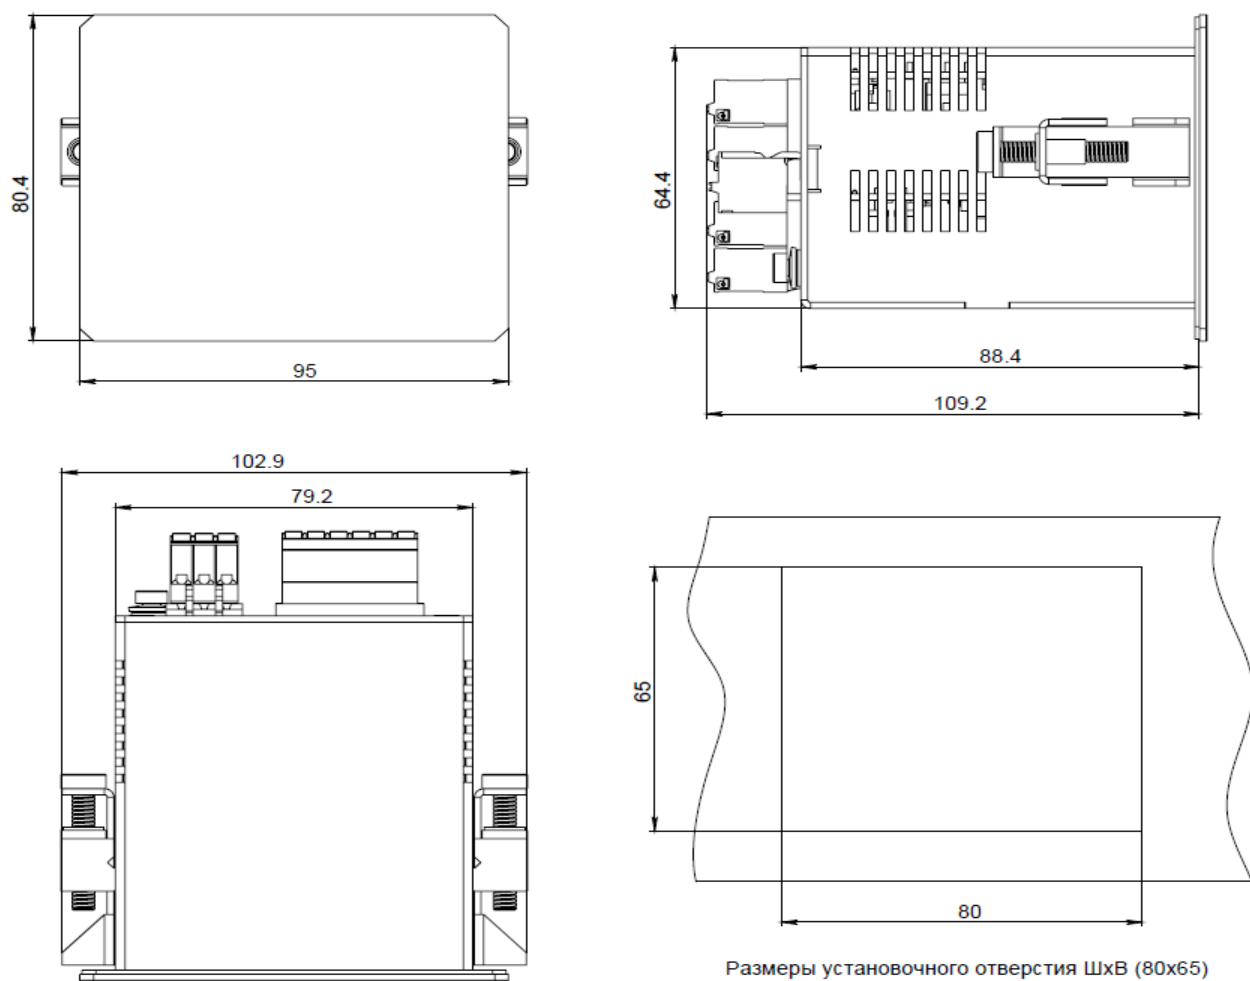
Габаритные размеры устройства и размер отверстия для монтажа
